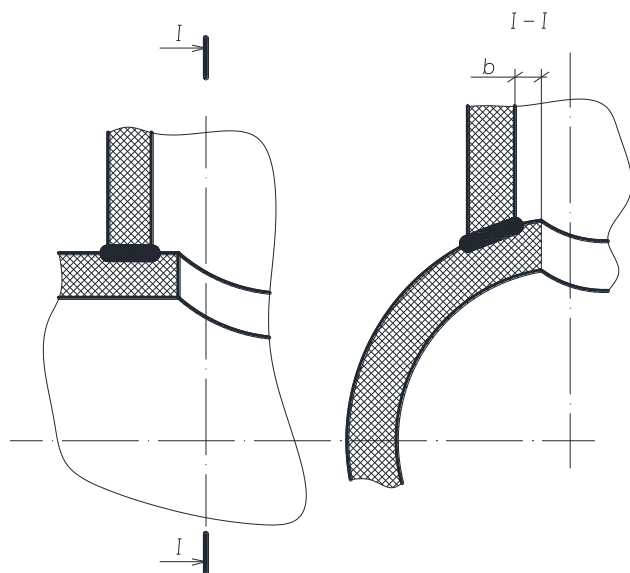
Конструктивные элементы шва сварного соединения (швы ТЗ)
